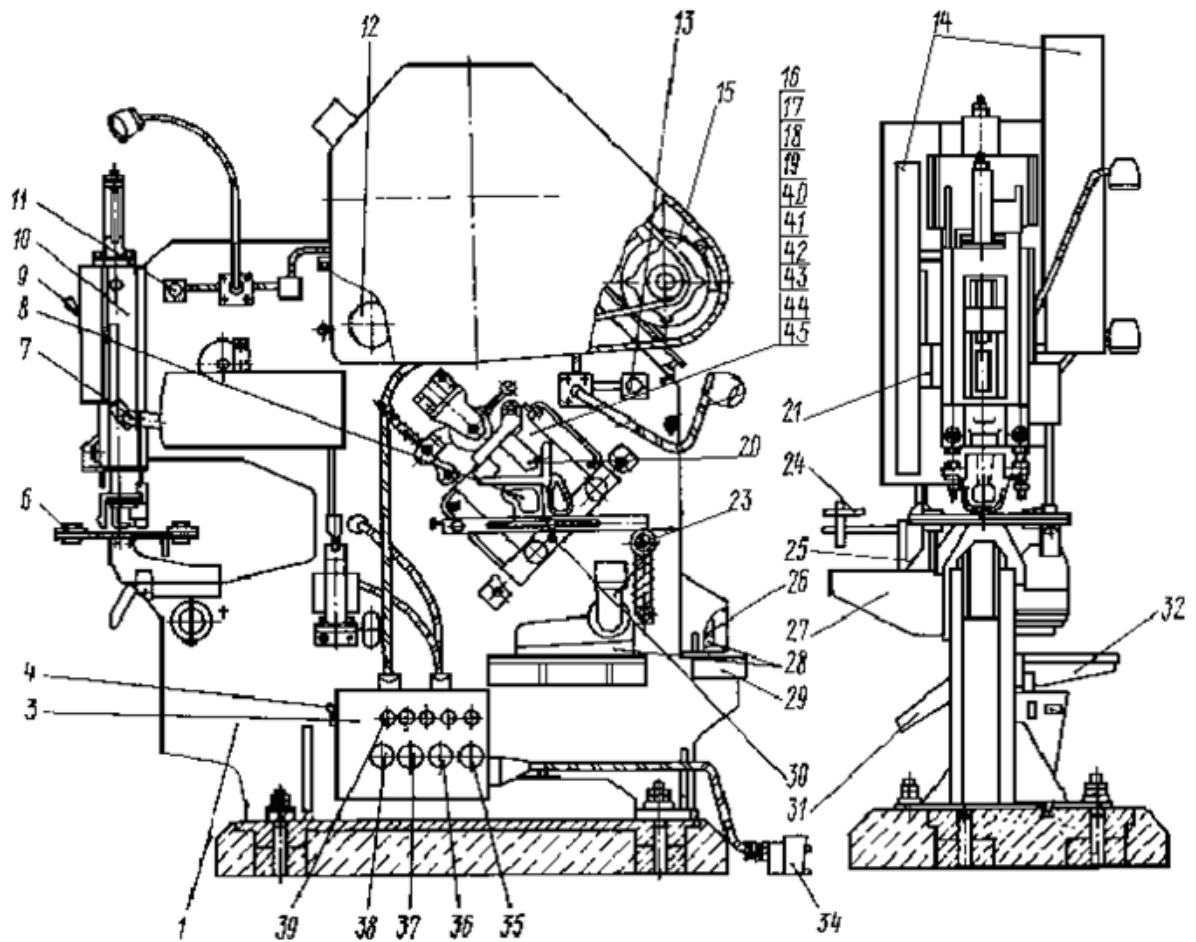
Расположение составных частей и органов управления пресс-ножниц НГ5222.
